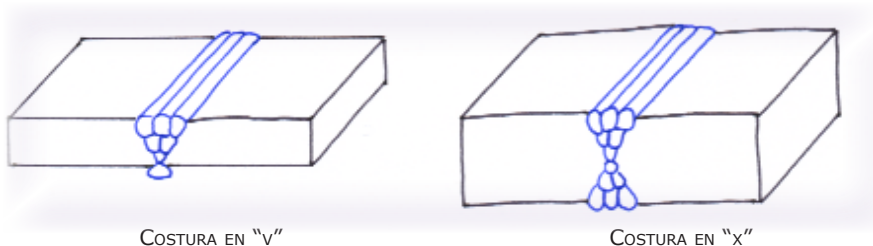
Tipos más importantes de costuras para soldadura con aire a presión
